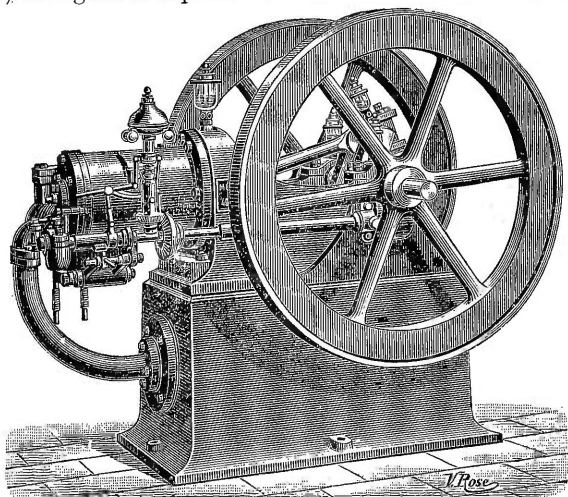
Vue d'ensemble du moteur à gaz Charon.
